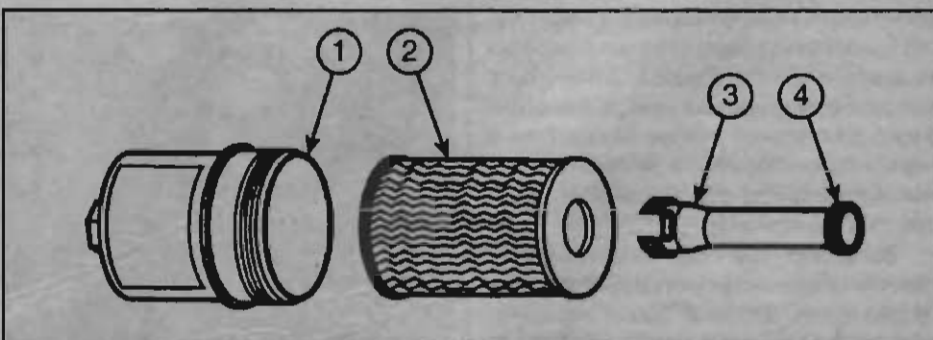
Бумажный фильтр картриджного типа: 1 – крышка масляного фильтра; 2 – фильтрующий элемент масляного фильтра; 3 – трубка; 4 – уплотнительное кольцо круглого сечения
